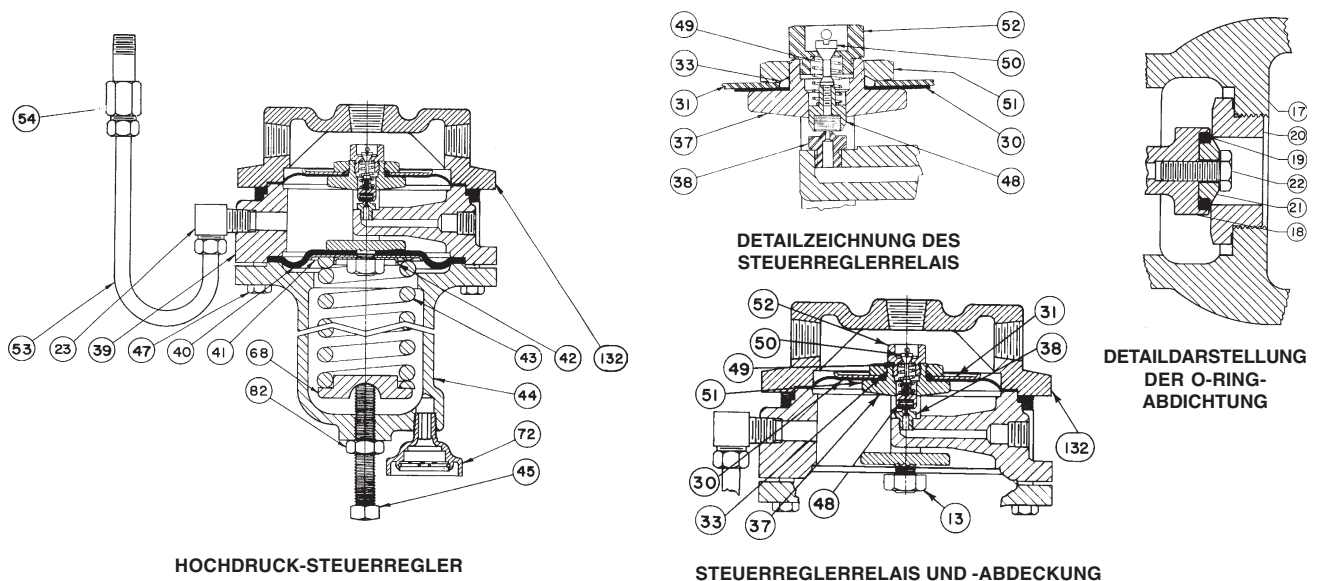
Druckregelgerät, Typ 99, mit Steuerregler 61L (Niedrigdruck) oder 61H (Hochdruck)
